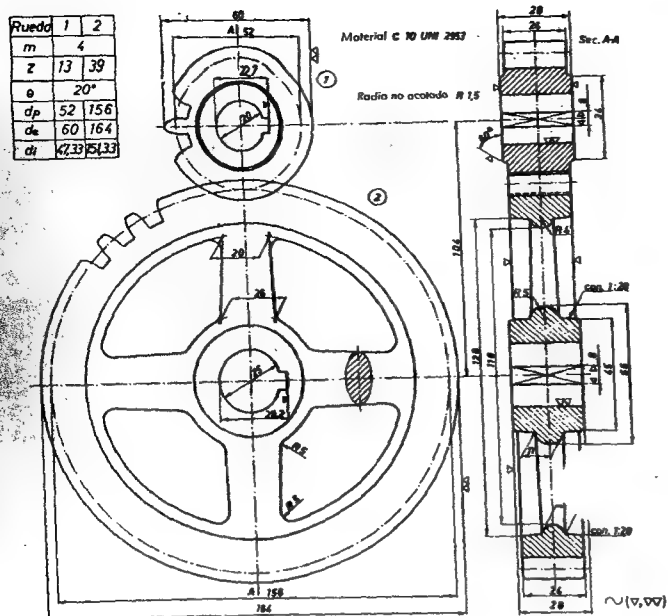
Juego de engranajes cilíndricos de dientes rectos.
